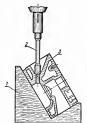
Установка головки цилиндров тракторного двигателя на деревянной подставке для растачивания
